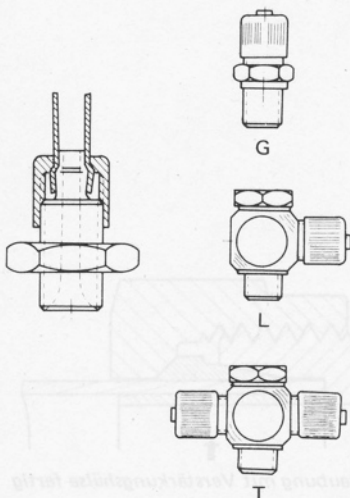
Verschraubungen für Kunststoffrohr (Bosch)
